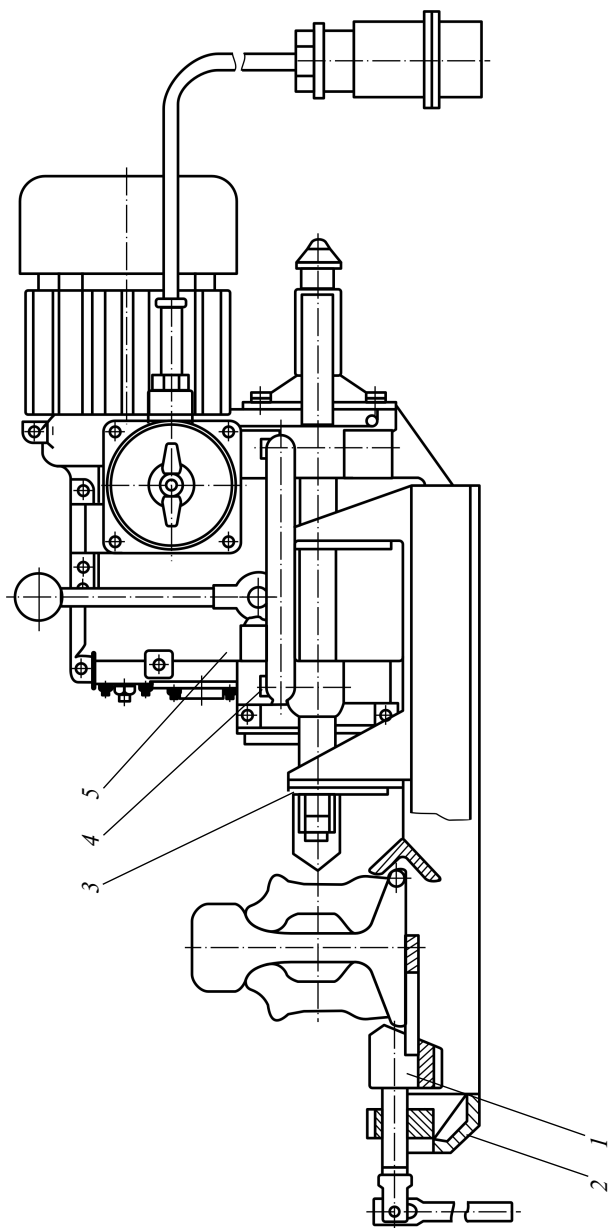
Рельсосоверлильный станок РСМ1М:
